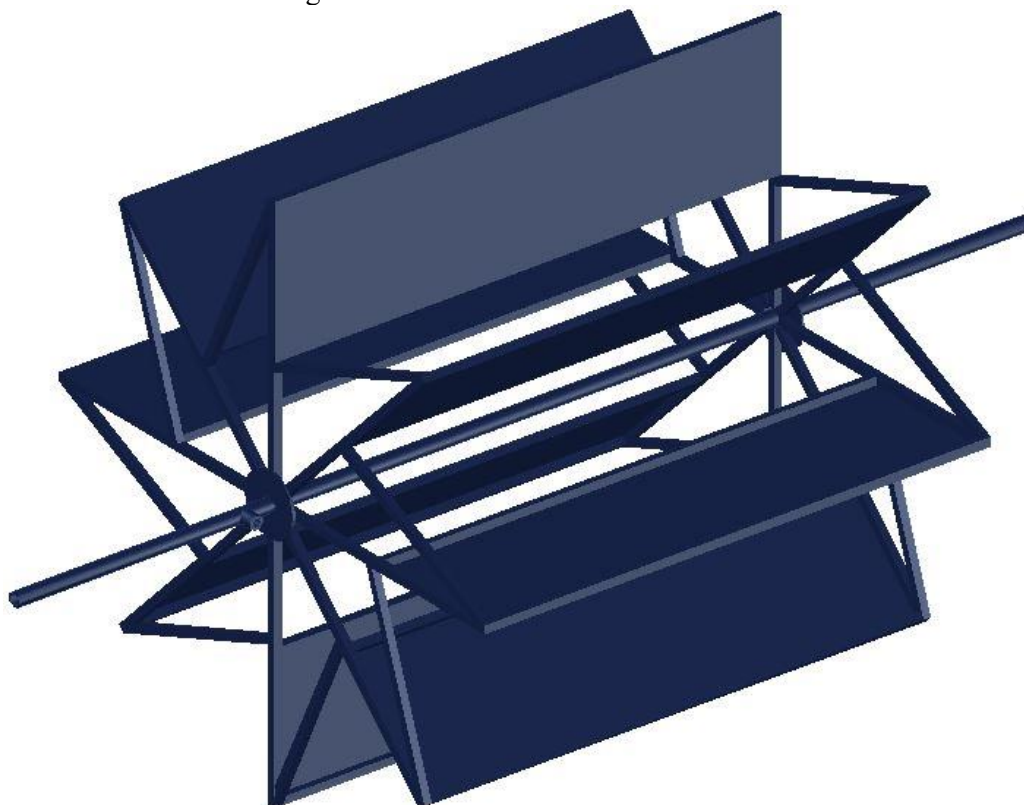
Vista explodida da estrutura da roda d'água e dos flutuadores.
